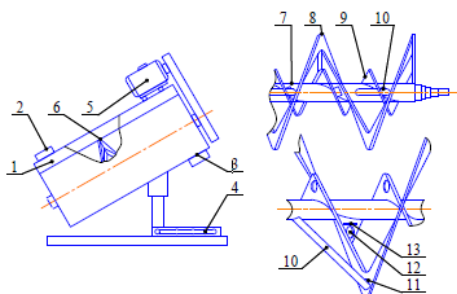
Змішувач за патентом № 2008082: 1 – корпус; 2, 3 – завантажувальний і розвантажувальний патрубки; 4 – рама; 5 – привід; 6 - змішувальний робочий орган; 7 – приводний вал; 8, 9 – зовнішня і внутрішня шнекові стрічки; 10 – жолоб; 11, 12, - отвори; 13 – пластина
